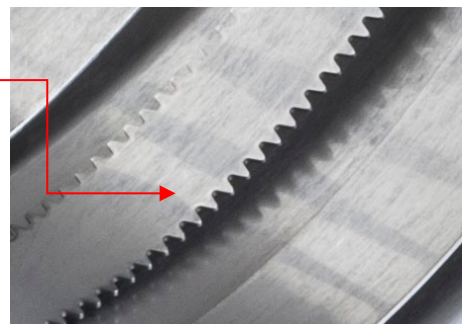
Pipe-Seal-Fix/-End einseitige Zahnreihe
